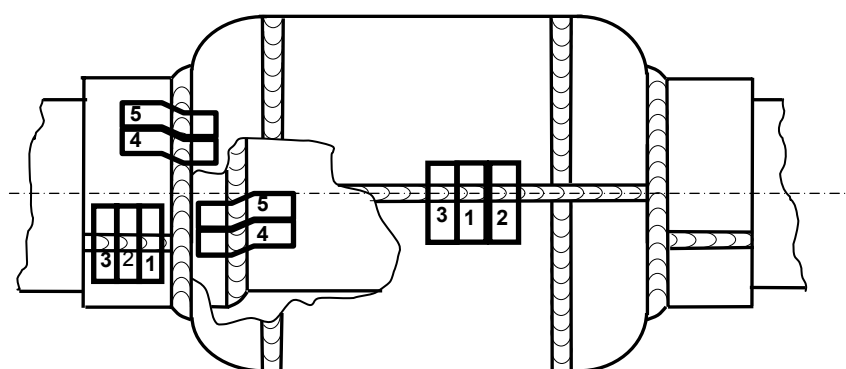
Схема вырезки образцов для проведения механических испытаний нахлесточных кольцевых угловых швов при аттестации технологий ремонта методом установки стальных сварных муфт:
